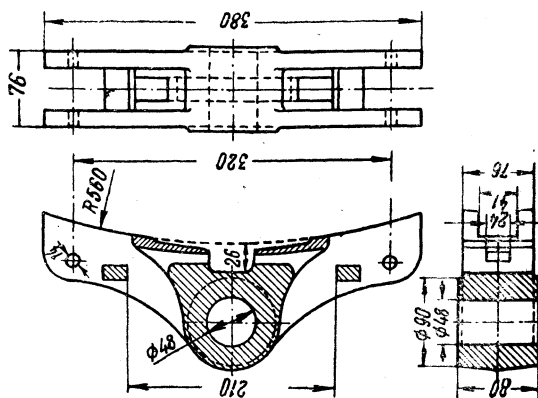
Башмак с посадкой на круглую цапфу и чековым креплением колодки ГОСТ 1204-41
